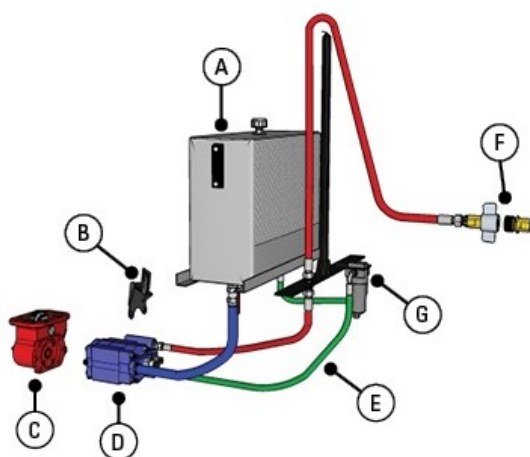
Příklad hydraulického sklápěcího mechanismu [14]
